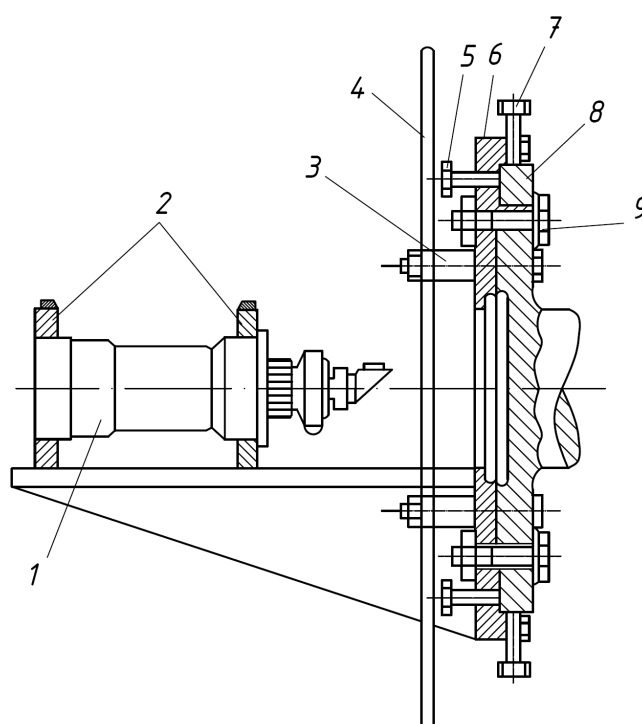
Пристосування для встановлення та центрування візирної труби на фланці вала двигуна:
